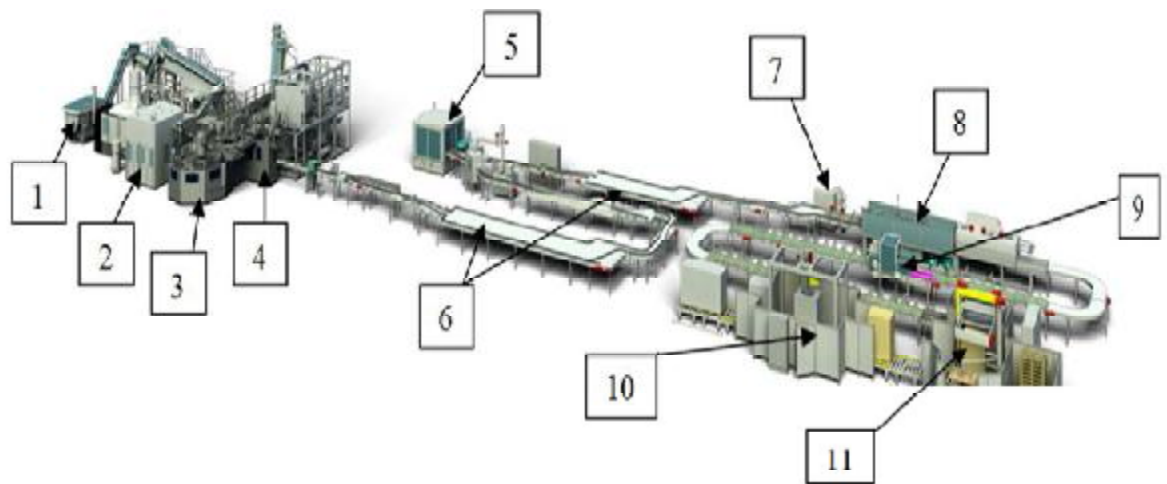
Emplacement des différentes machines de la chaîne [2].
